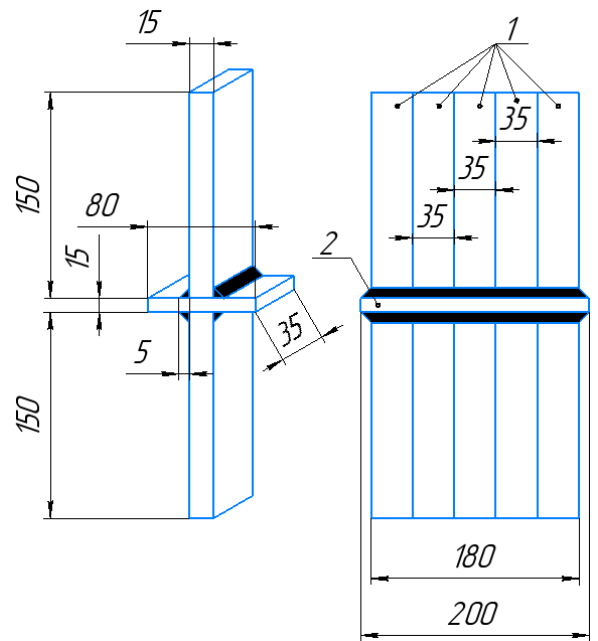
Загальний вигляд хрестоподібного зразка без надрізу
